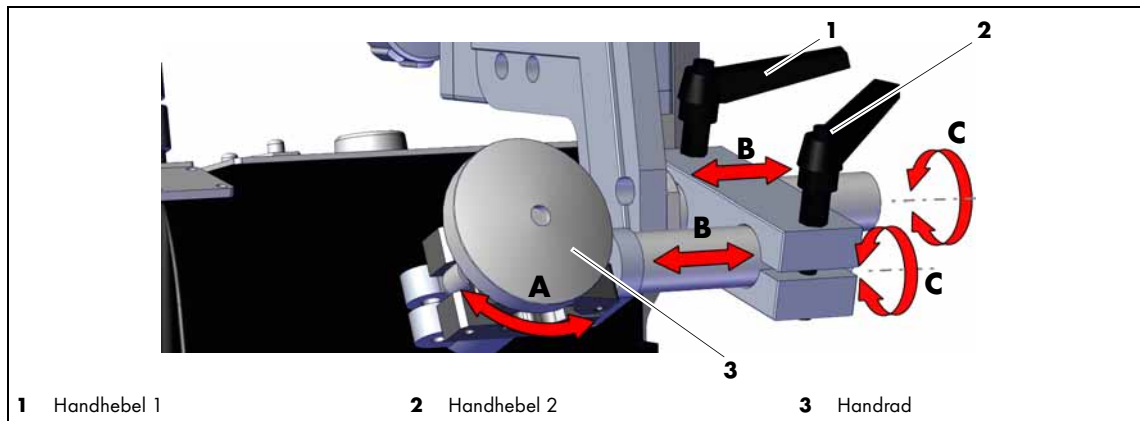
Einstellmöglichkeiten für die Position und die Neigung des Schweißbrenners
